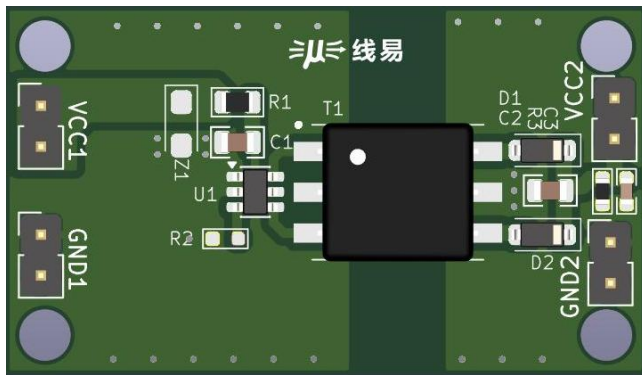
PCB 版图正面 (尺寸: 23x 40mm)
